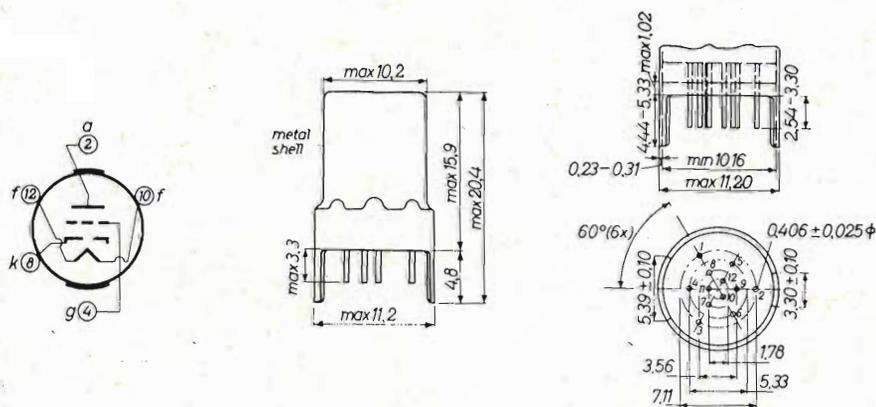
Dimensioni d'ingombro (mm) e collegamenti agli elettrodi. I piedini 1, 3, 5, 6, 7 e 9 sono collegati internamente. Il piedino 11 è stato omesso.
